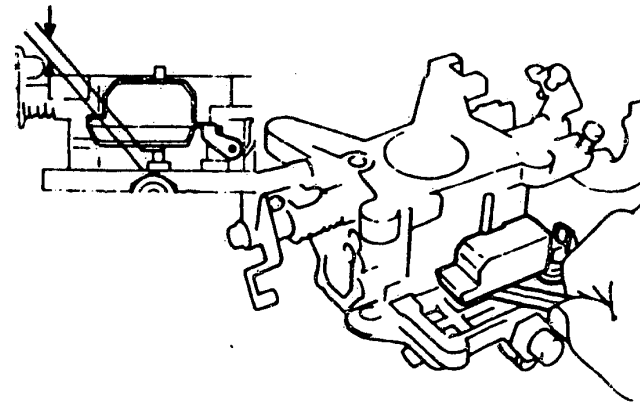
Das Messen des Schwimmers bei umgekehrtem Gehäuse. Schwimmers ohne Dichtung 5,4 mm. Er kann mit einer Rundlehre gemessen werden.
